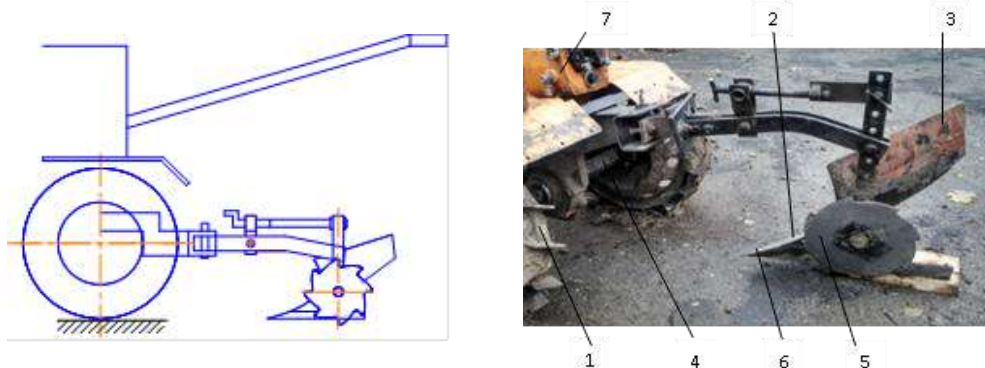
Схема і загальний вигляд модернізованого агрегату для оранки дачних ділянок: 1 – металеве колесо; 2 – груди; 3 – відвал; 4 – відцентровий самоблокувальний механізм (диференціал); 5 – дисковий ніж; 6 – леміш; 7 – трансмісія мотоблока.
